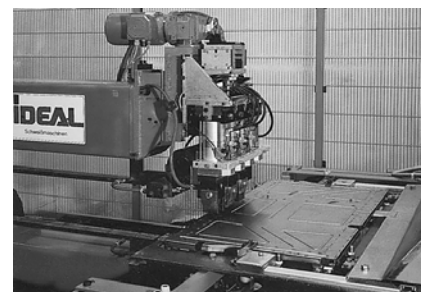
Координатный промышленный робот точечной и рельефной сварки в кондукторах CSR 302
